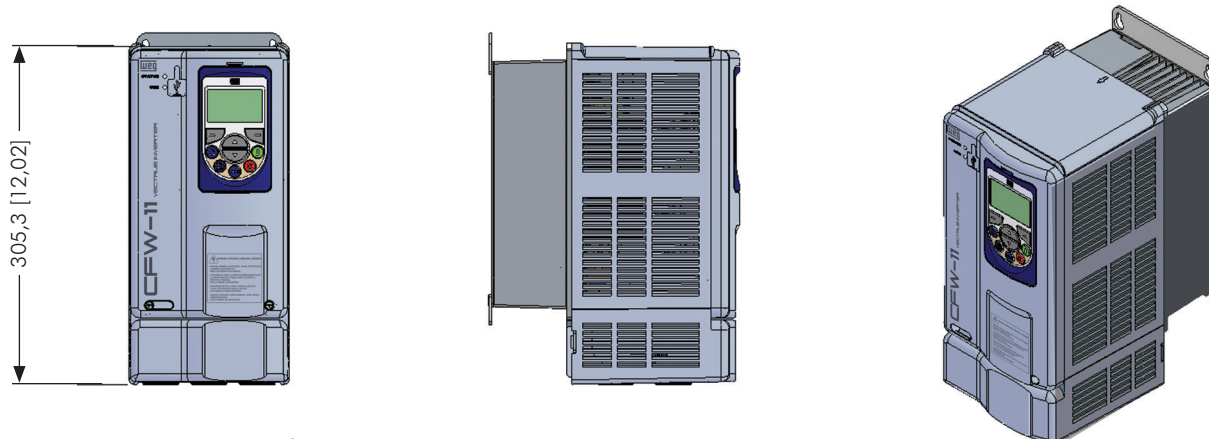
Afmetingen omvormer - framemaat C - mm [in]
